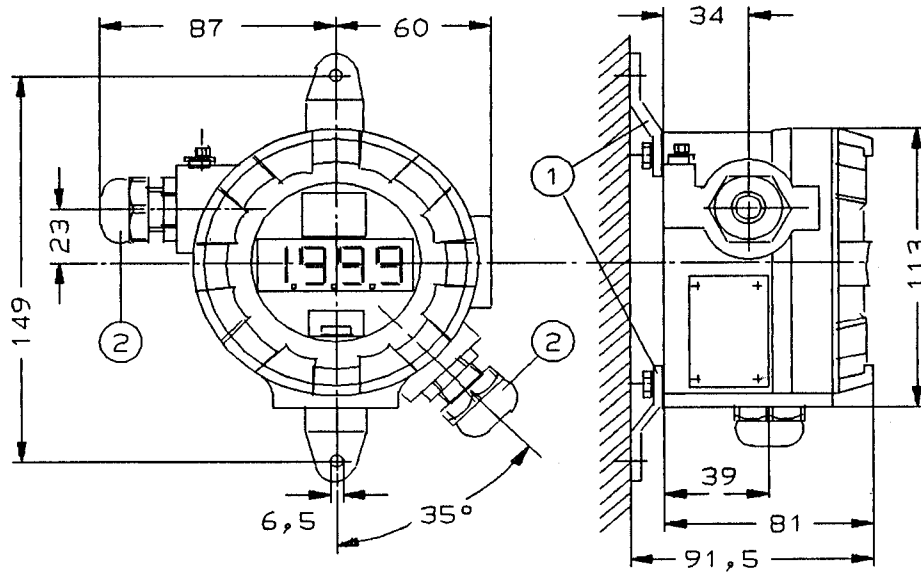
Abmessungen mit Befestigungslaschen für Wandmontage
